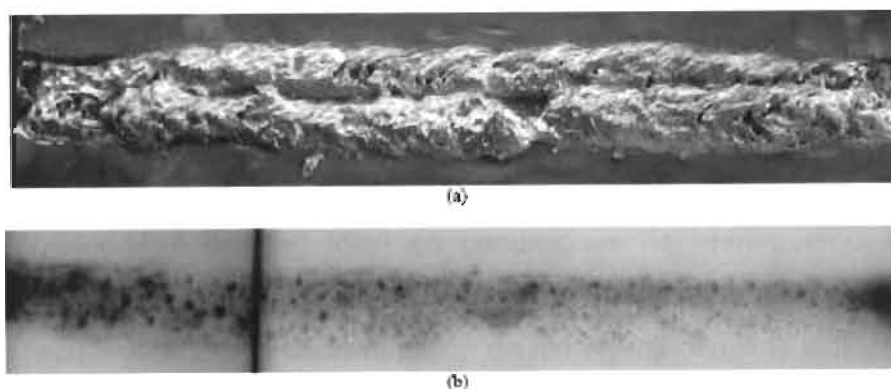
Técnicas utilizadas en la actualidad de soldadura marina <sup>[1]</sup>
